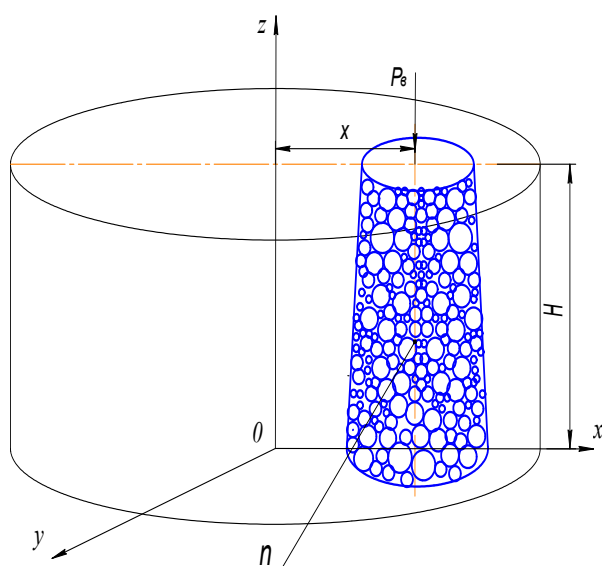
Расчетная схема элемента n порошка для цилиндрической прессовки
